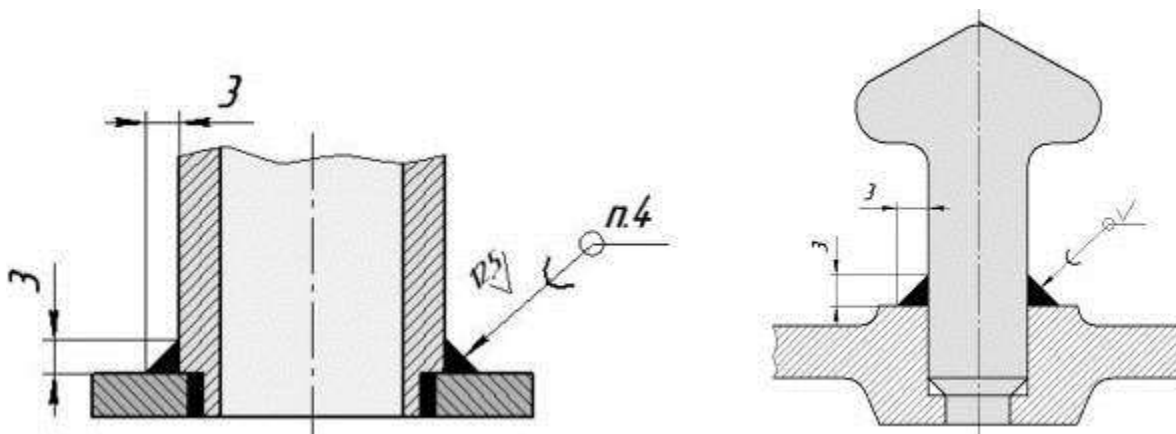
Примеры нанесения на чертёж паяного шва размеров и обозначение шероховатости
